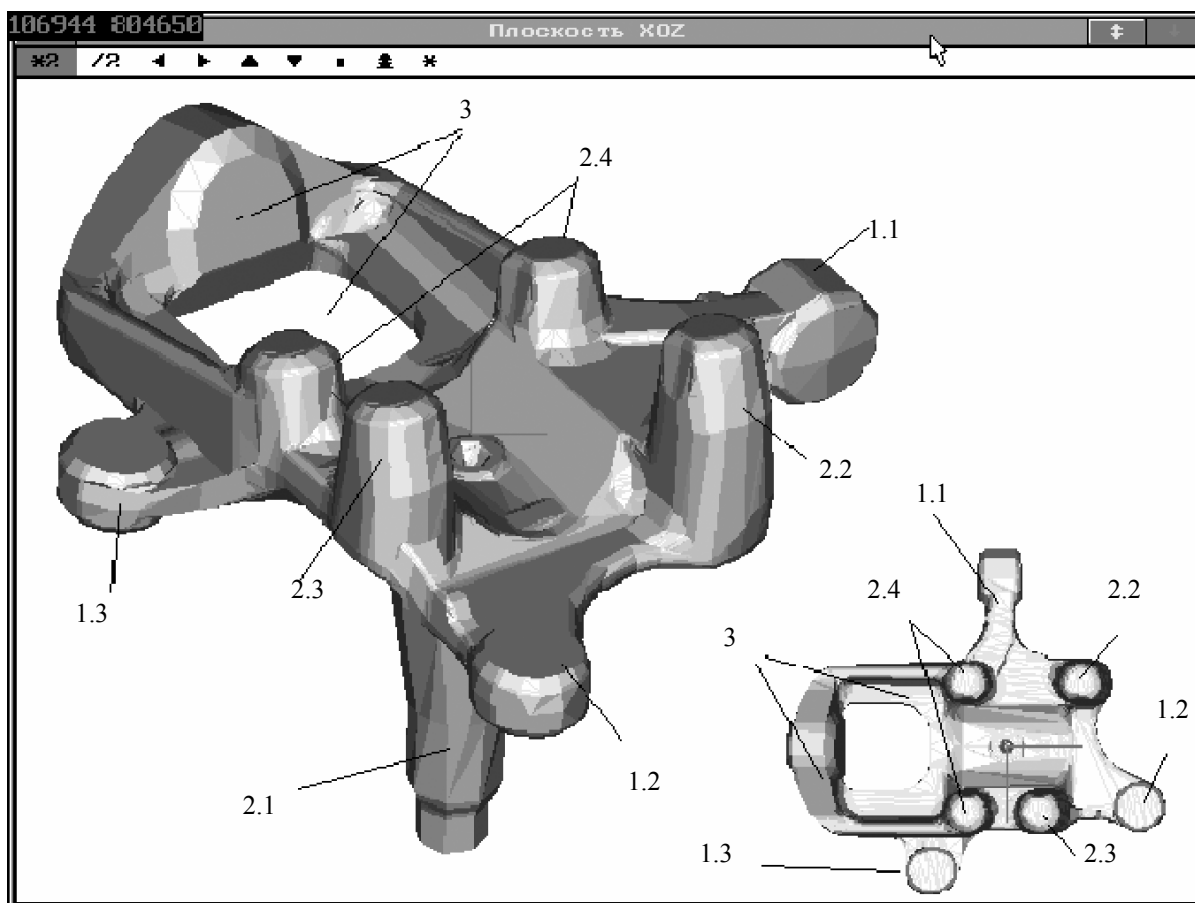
Основные конструктивные элементы поковки поворотного кулака.
